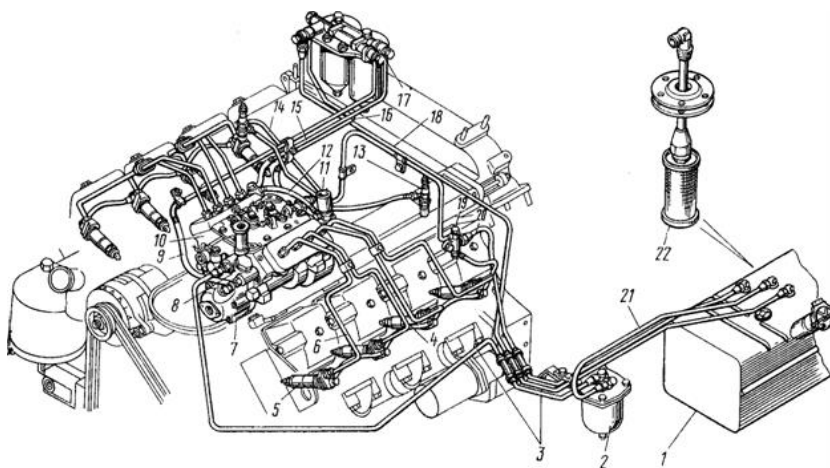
Схема питания двигателя топливом: 1 – бак топливный; 2 – фильтр грубой очистки топлива; 3 – трубка топливная подводящая к насосу низкого давления; 4 – трубка топливная дренажная форсунок левых головок; 5 – форсунка; 6 – трубка топливная высокого давления; 7 – насос топливоподкачивающий низкого давления; 8 – насос топливоподкачивающий ручной; 9 – трубка топливная отводящая насоса низкого давления; 10 – насос топливный высокого давления; 11 – клапан электромагнитный; 12 – трубка топливная к электромагнитному клапану; 13 – свеча факельная; 14 – трубка топливная дренажная форсунок правых головок; 15 – трубка топливная подводящая ТНВД; 16 – трубка топливная отводящая ТНВД; 17 – фильтр тонкой очистки топлива; 18 – трубка топливная фильтра тонкой очистки топлива; 19 – тройник крепления топливных трубок; 20 – трубка топливная сливная; 21 – топливопровод к фильтру грубой очистки; 22 – труба приемная с фильтром
